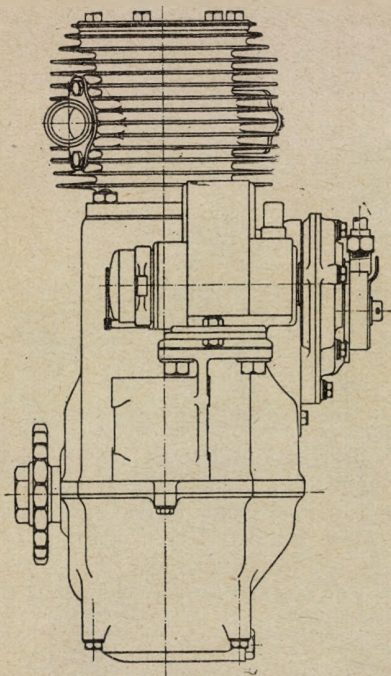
Jednoválcový motor „Barr a Stroud“.
